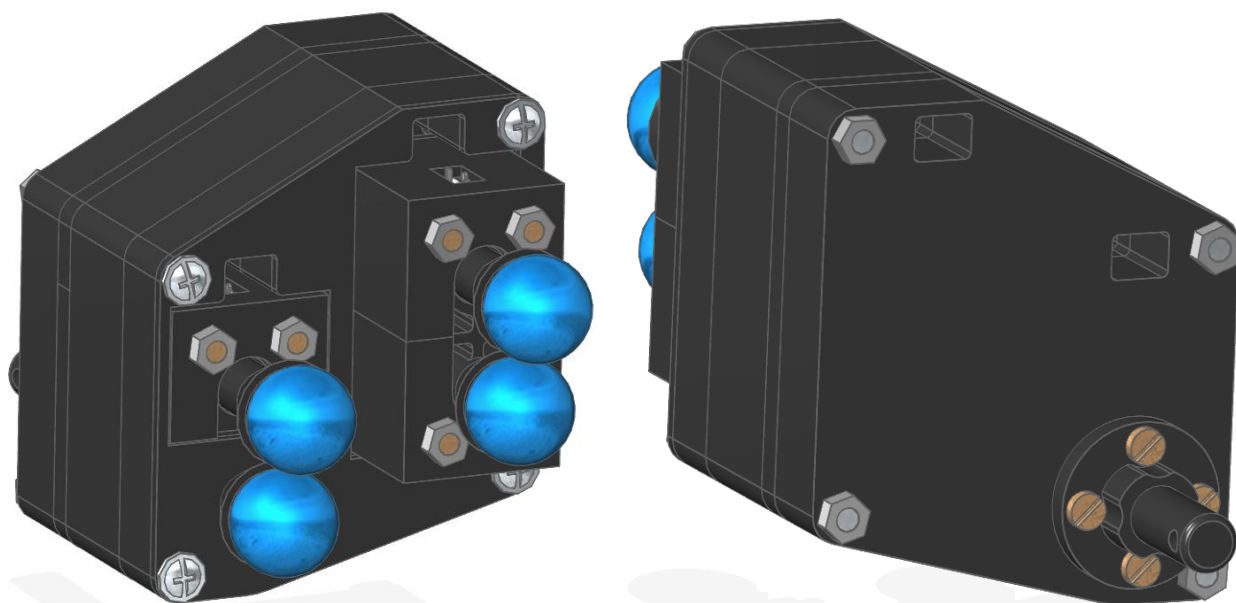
Protótipo do Conjunto de Sensores - Montagem completa.
